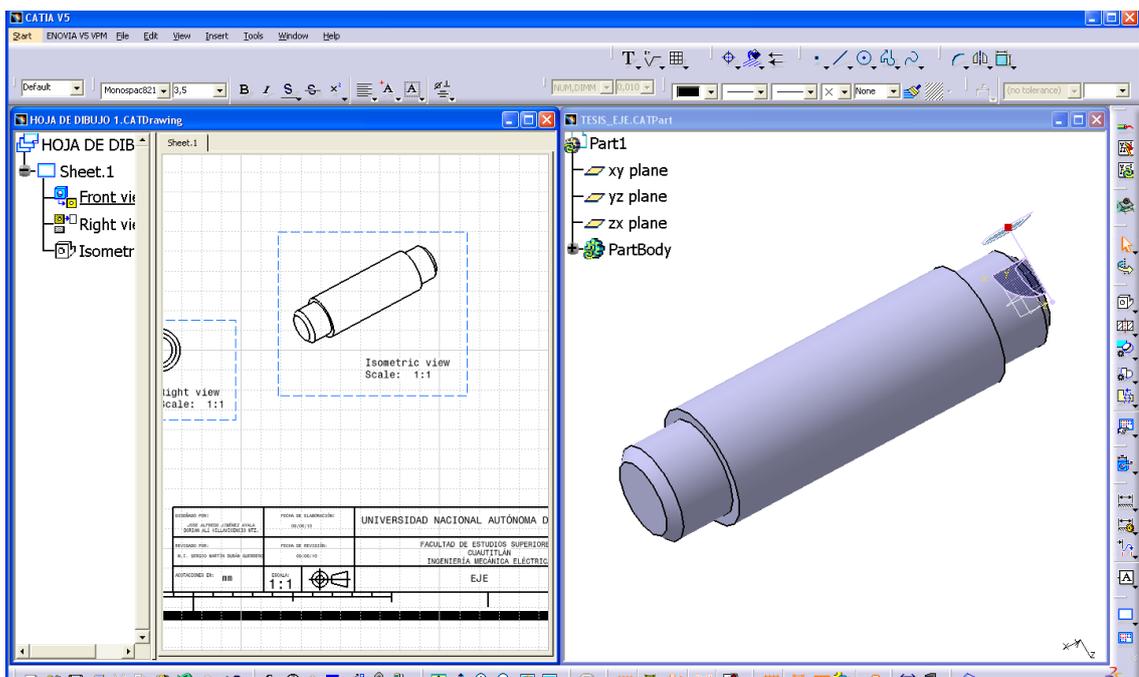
Vista isométrica del eje en la ventana drafting.
